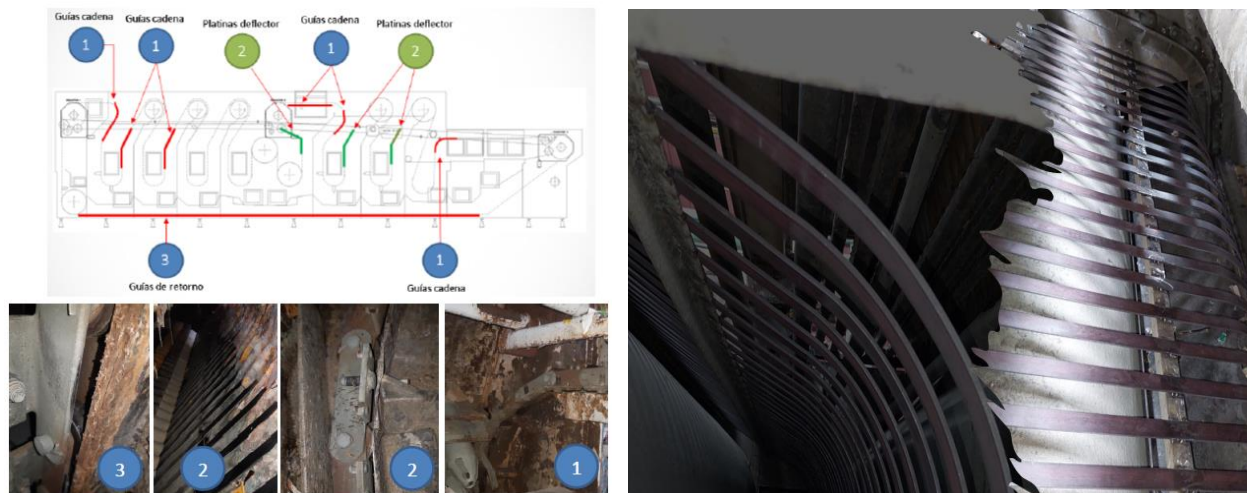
Intervención en la zona de prelavado en lavadora de botellas (antes y después de la intervención)
